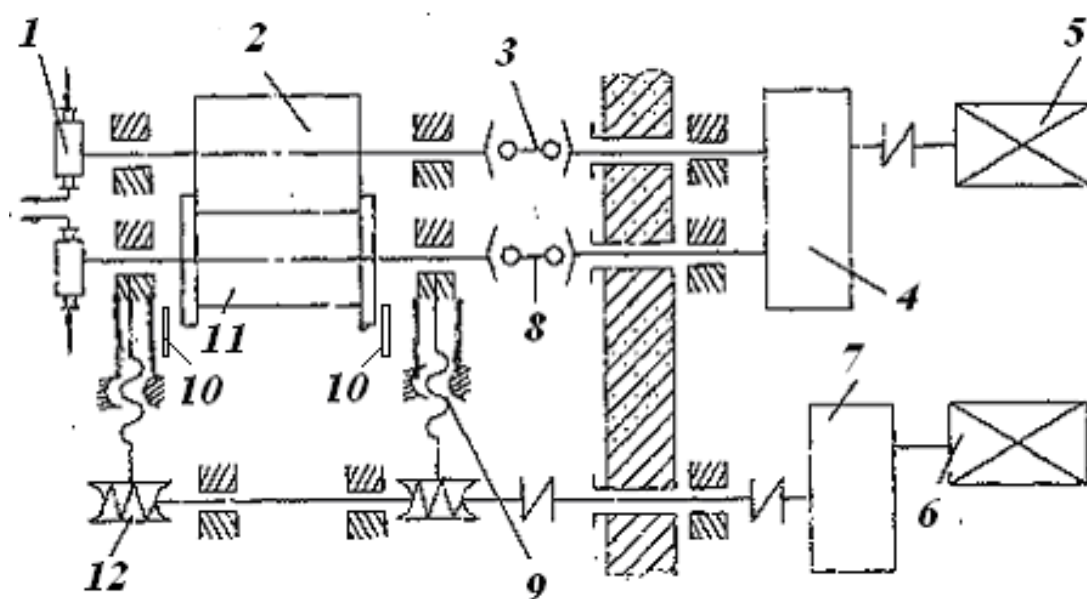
Кинематическая схема типовой вальцевой установки [8]:
